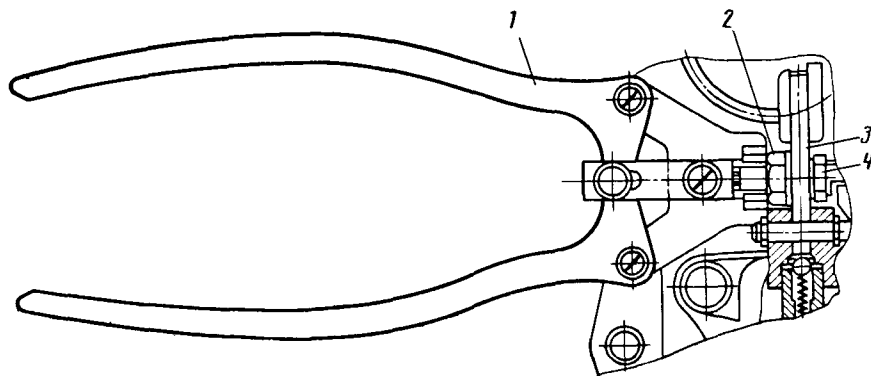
Щипцы для фиксации гайки регулировочного винта вилки включения заднего хода: 1 — щипцы; 2 — регулировочная гайка; 3 — вилка включения заднего хода; 4 — регулировочный винт
